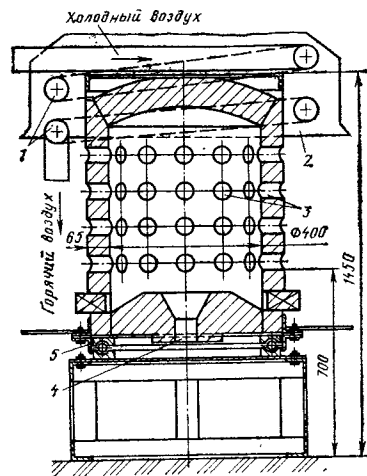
Очковая вращающаяся печь для нагрева концов заготовок при штамповке гаек и высадке головок болтов и заклепок:
